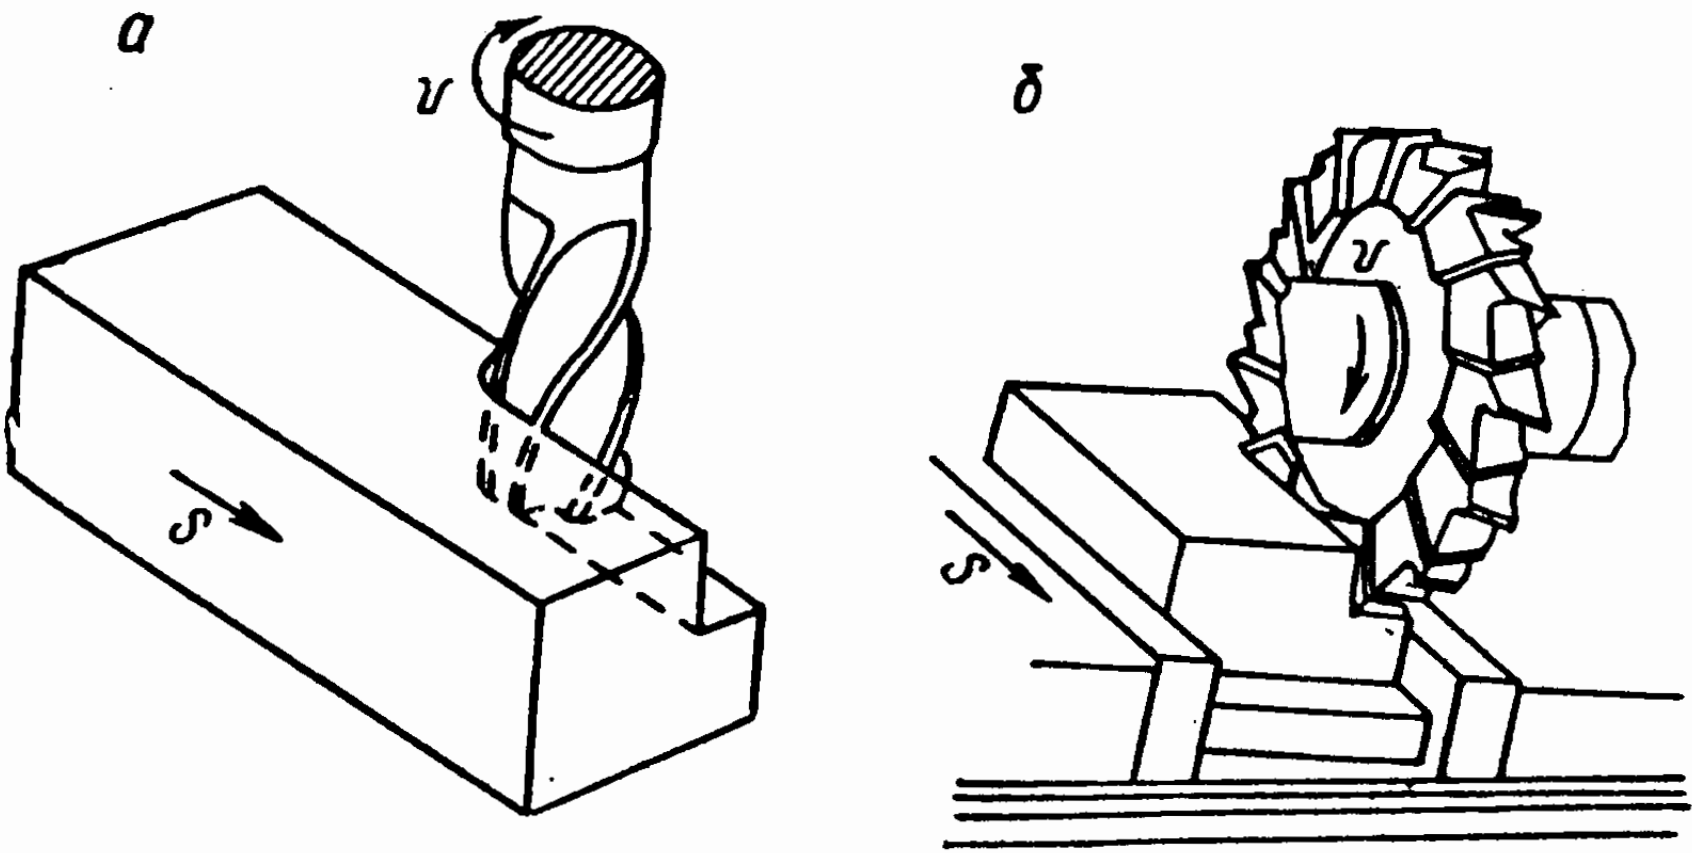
Фрезерование уступа концевой и дисковой фрезой.
